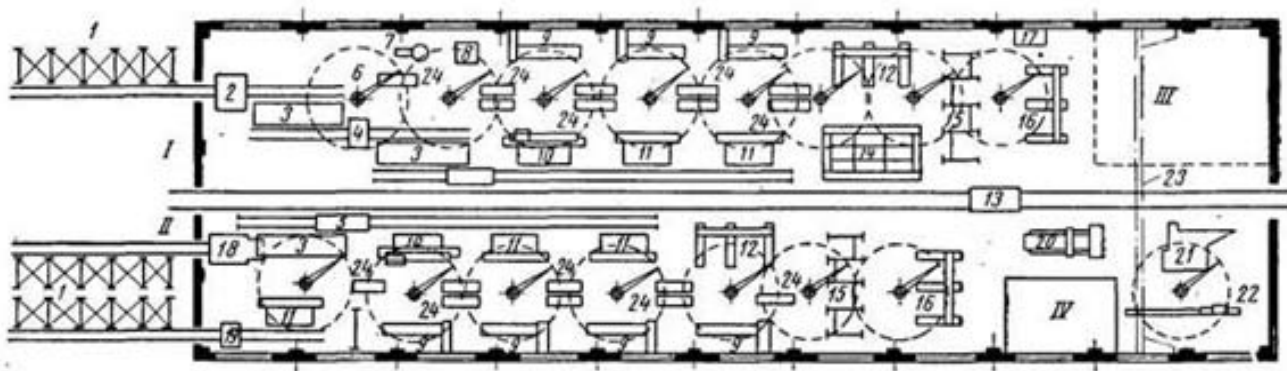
Схема планування трубозаготівельного цеху:
